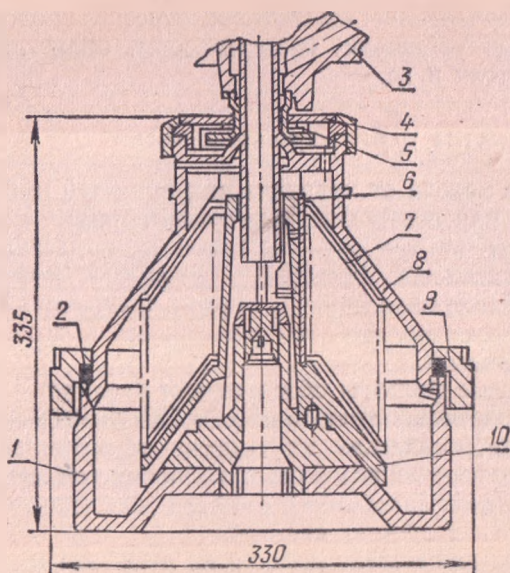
Барабан полугерметического сепаратора-очистителя:
